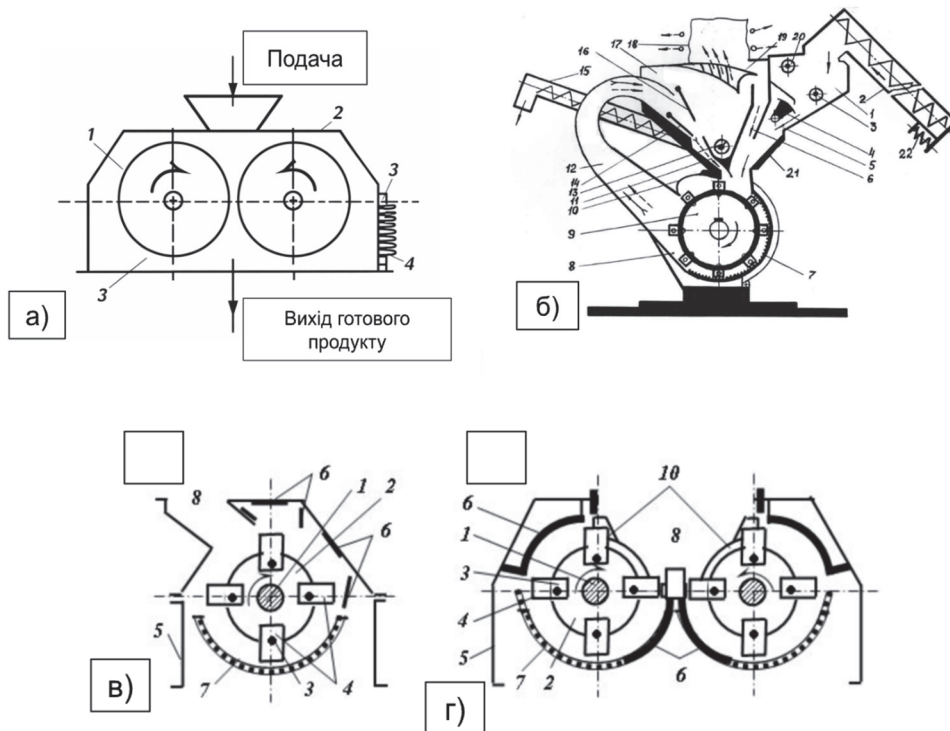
Конструктивні схеми дробарок зернистих матеріалів:
